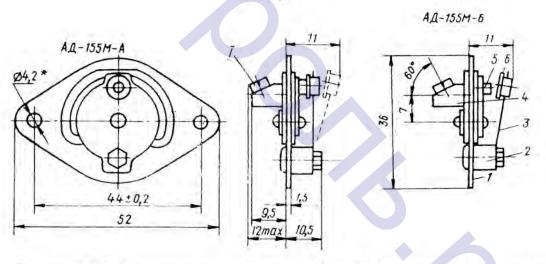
Термовыключатель типа АД-155М без защитного колпачка (размеры без допусков наибольшие):
